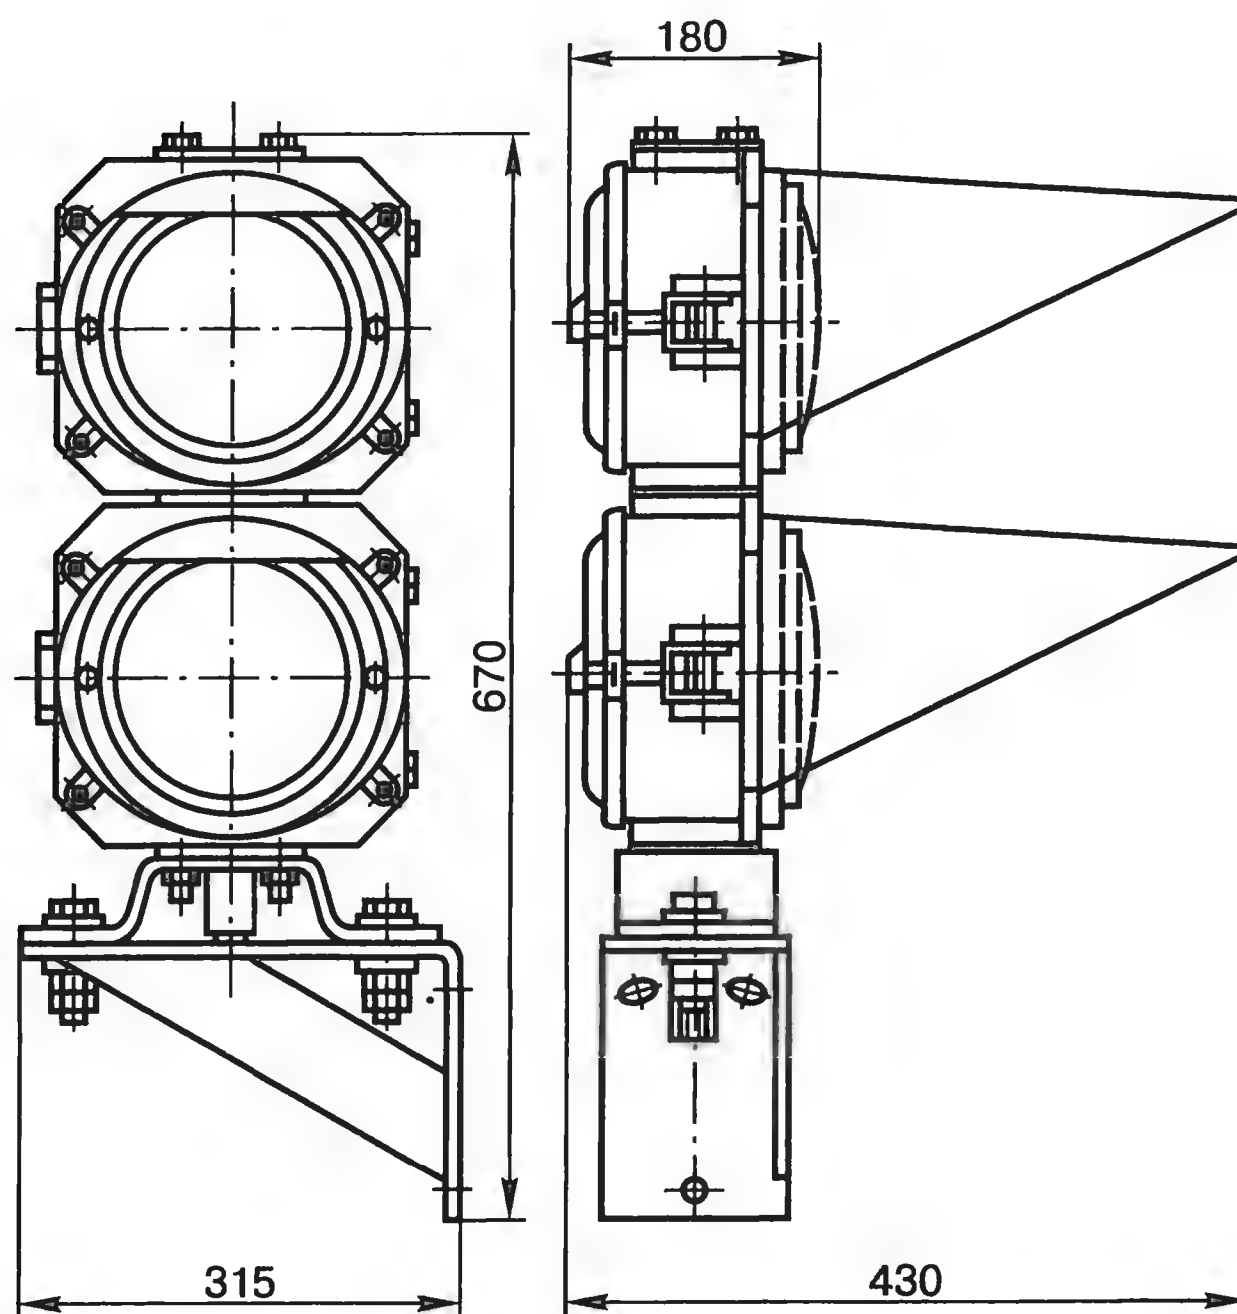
Двухзначный линзовый светофор типа «Метро»
